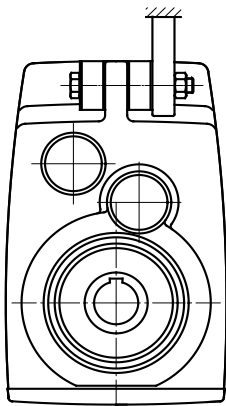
Motorreductor op as zonder installatiesteun met gemonteerd bevestigingelement
